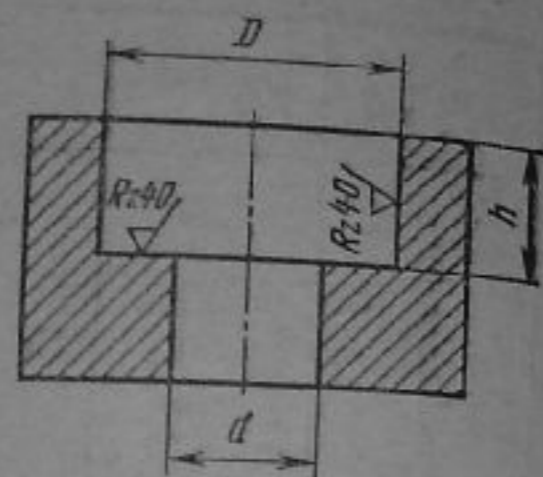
Эскиз обрабатываемой поверхности заготовки к задаче 47
